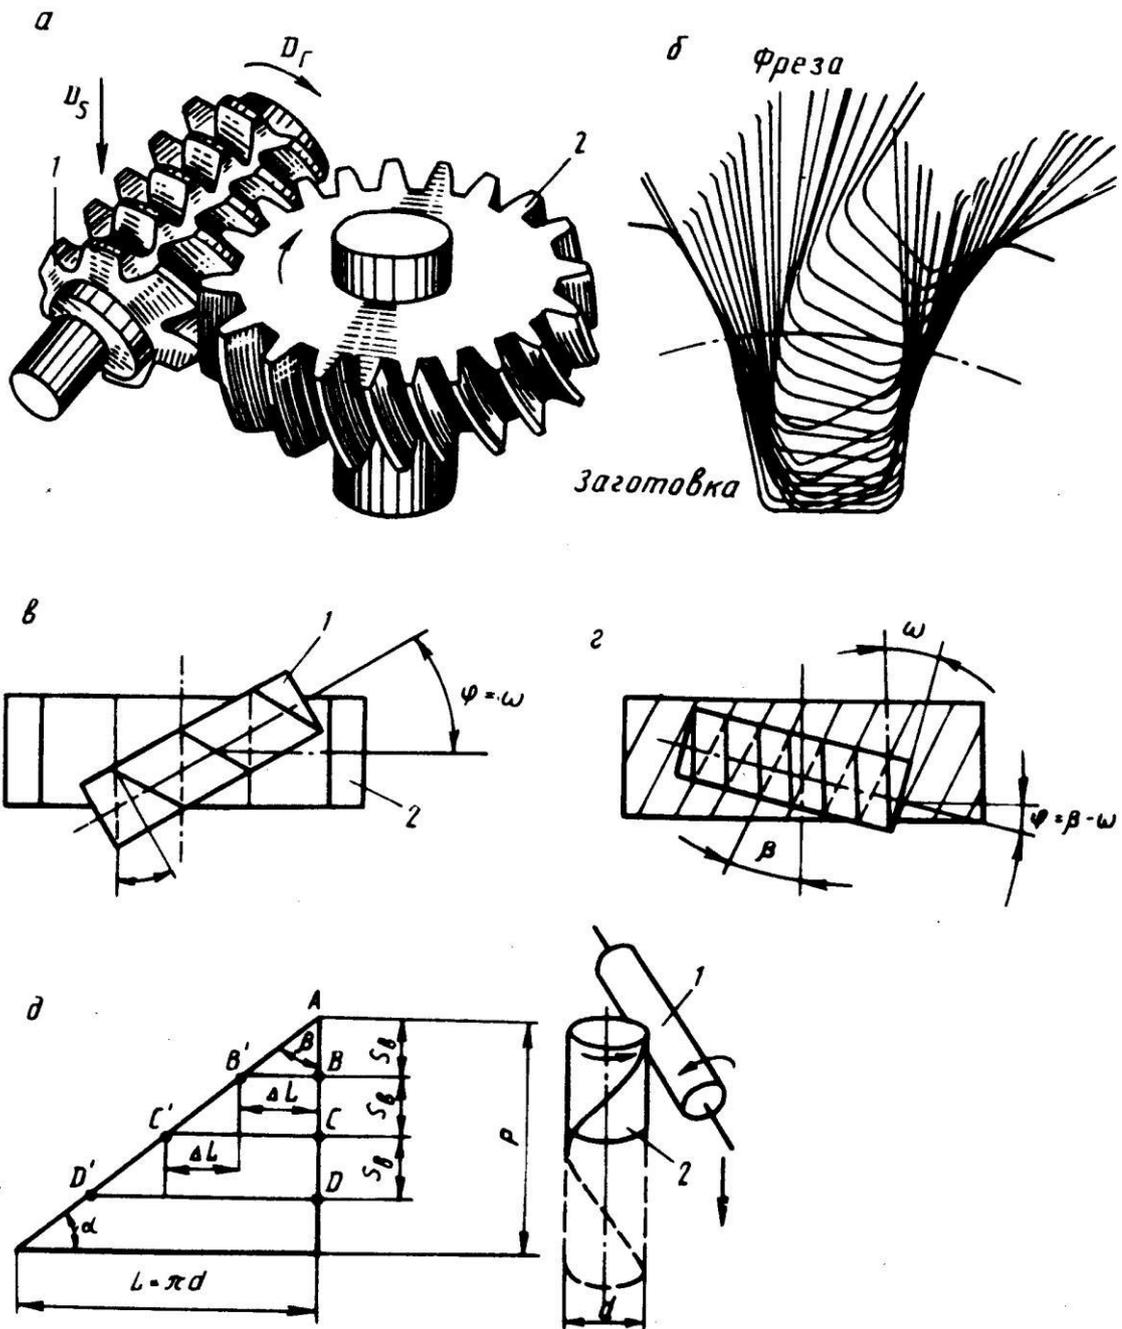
Схемы нарезания цилиндрических зубчатых колес червячной фрезой
